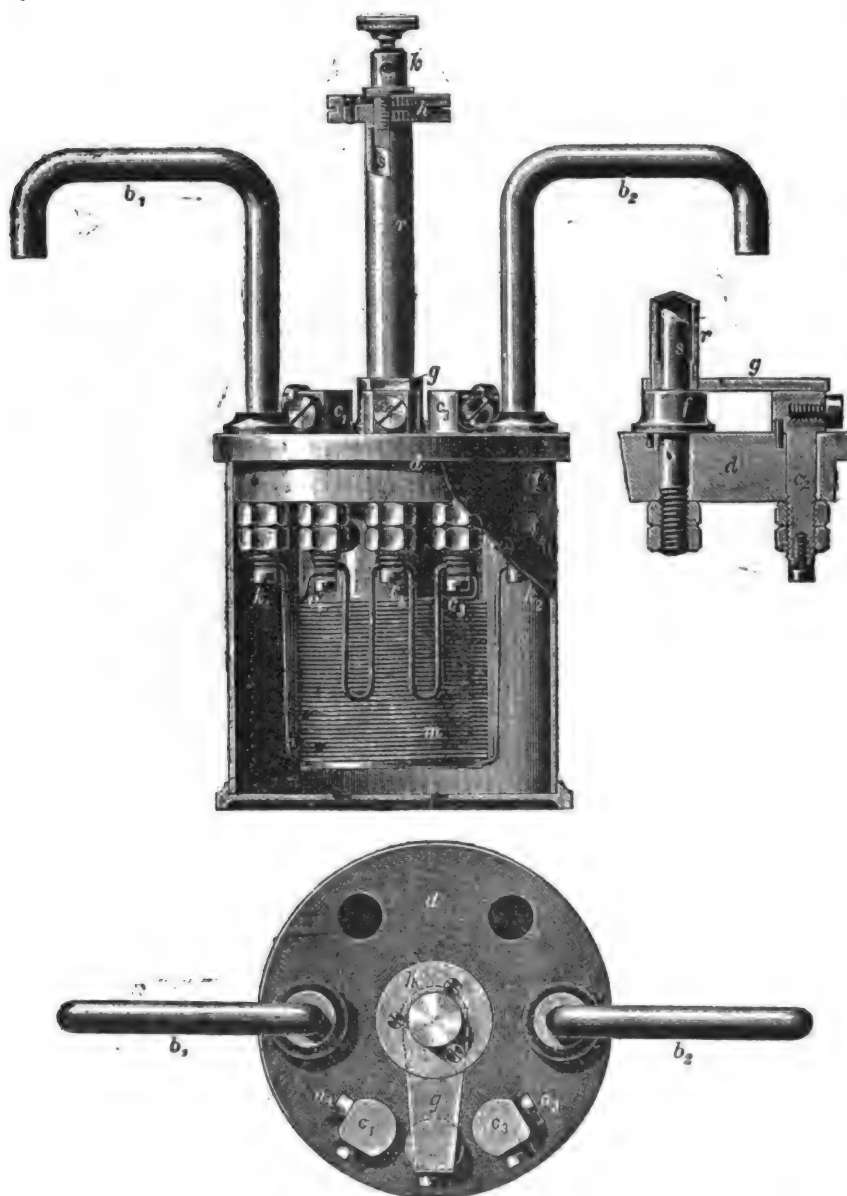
, 4 et 5. — Elévation plan et détail d'une boîte de bifurcation
